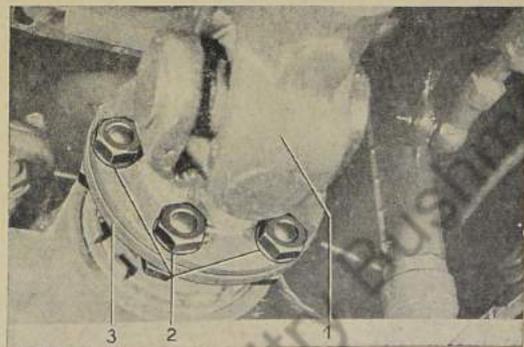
Vordere Längsgelenkwelle von der Flansch- welle abschrauben
